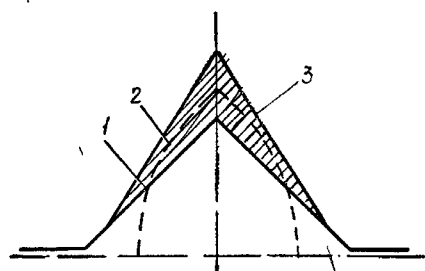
Диаграмма опережения по контуру квадратного калибра при прокатке в нем овала: 1 — калибр; 2 — заготовка; 3 — распределение опережения.
